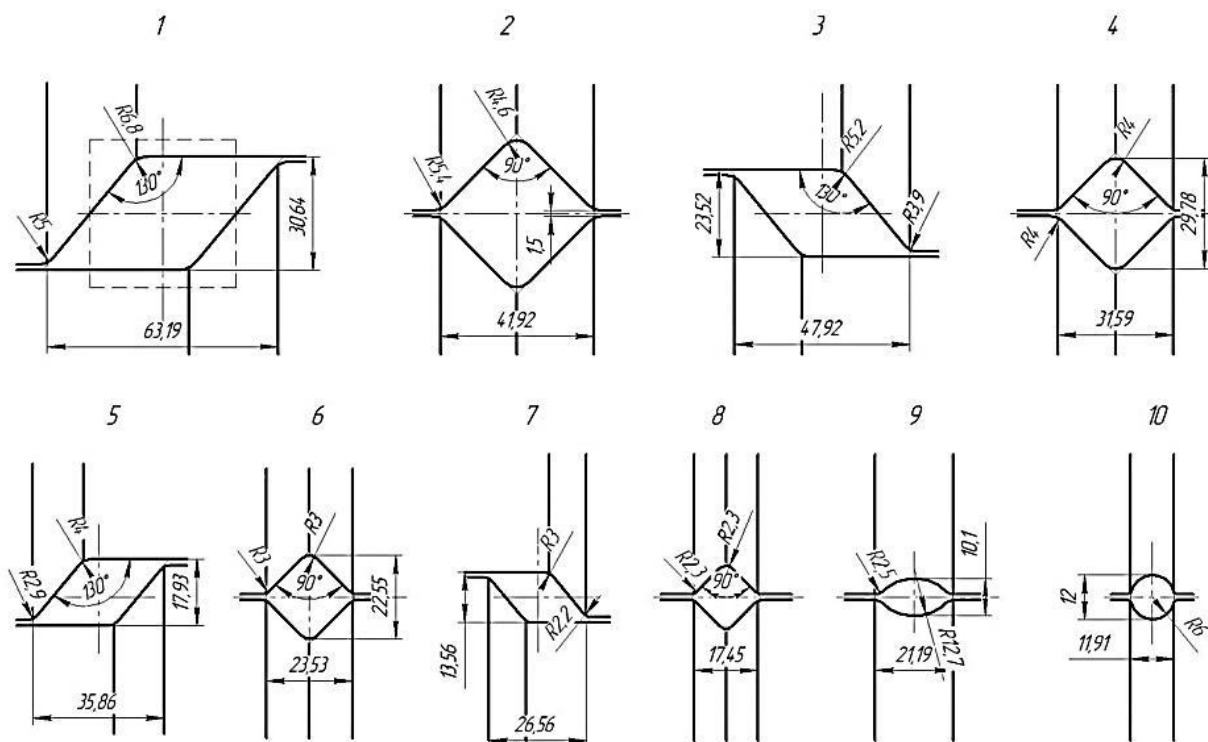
Схемы калибровки валков лабораторного стана «ДУО 200/150» (1–10 номера проходов)
